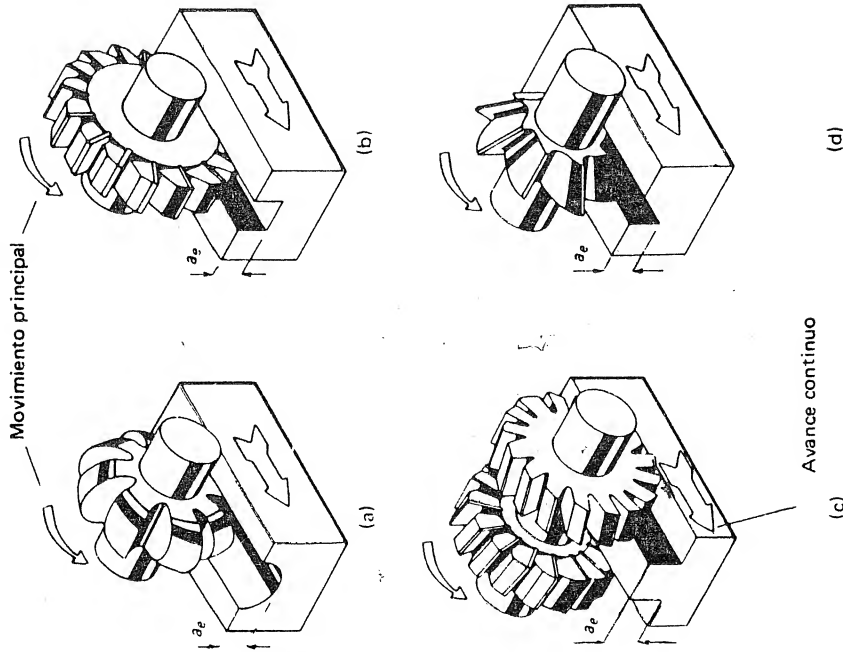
Algunas operaciones de fresado horizontal. (a) Fresado de forma; (b) ranurado; (c) fresado compuesto; (d) fresado angular.
